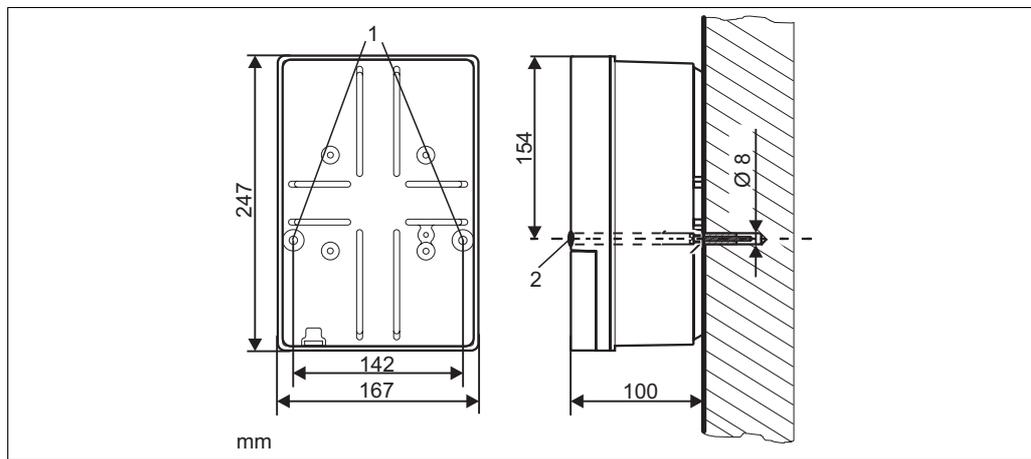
Dimensioni per il montaggio a parete, vite di fissaggio: Ø 6 mm, presa a parete: Ø 8 mm
